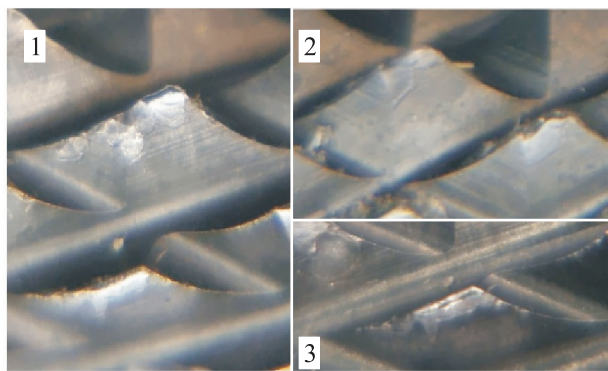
Внешний вид изношенных режущих кромок концевых фрез фирмы AXIS
